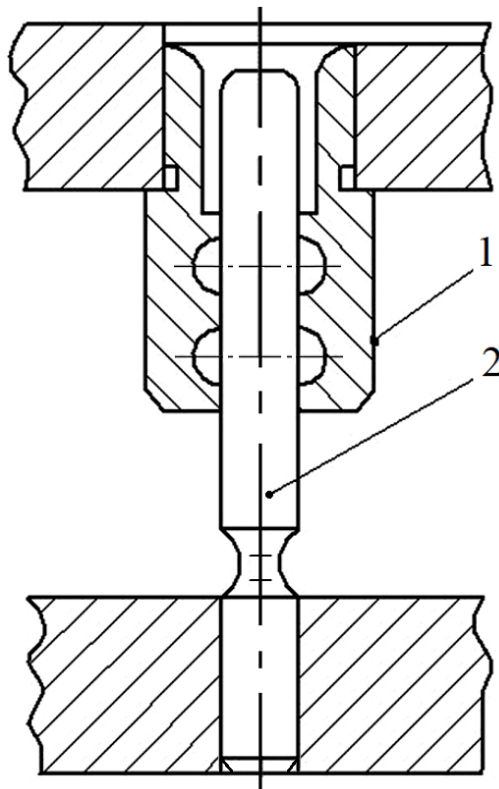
Загальний вигляд циліндричного напрямного вузла ковзання штампа:
